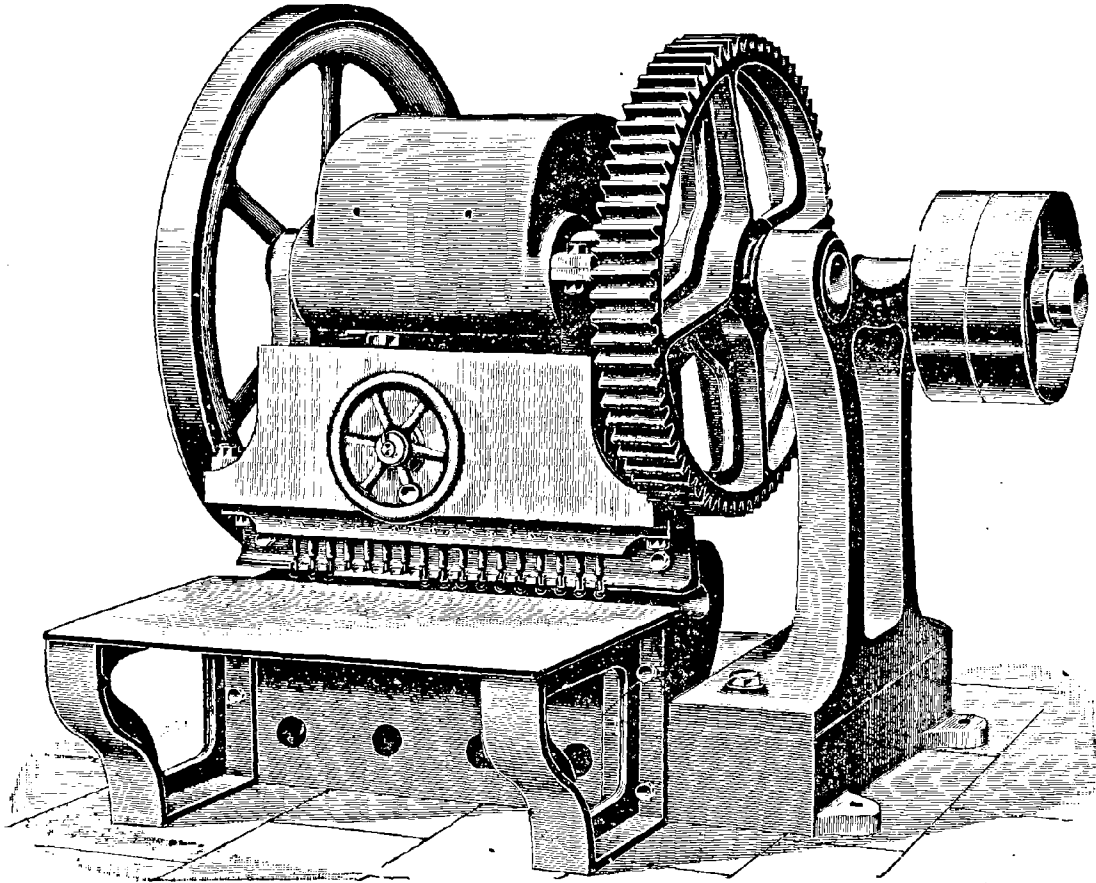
Machine à poinçonner multiple de M. Lucas.
